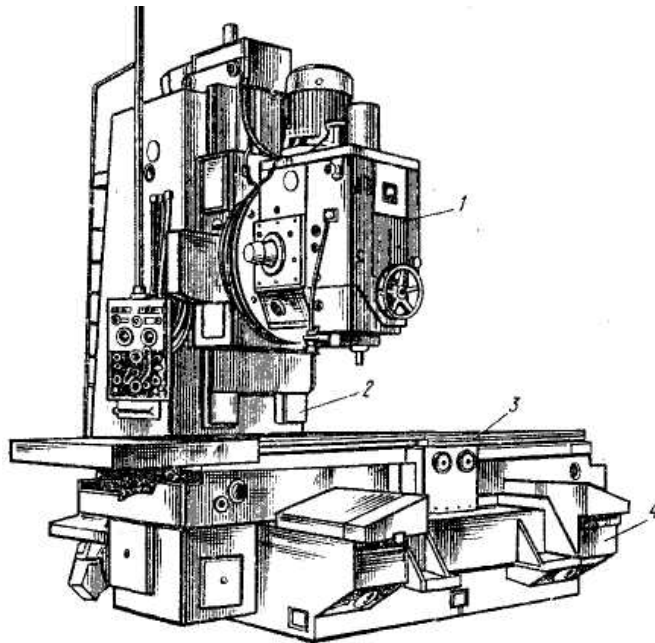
Бесконсольный фрезерный станок: 1 – шпиндельная головка; 2 – стойка; 3 – стол; 4 – массивная станина
